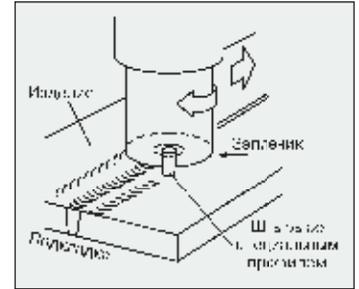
Схема процесса сварки трением с перемешиванием
